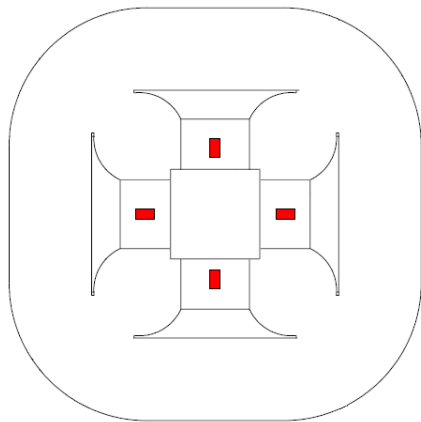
Vista de planta de um *stool*. Em destaque, a posição dos extensômetros.
